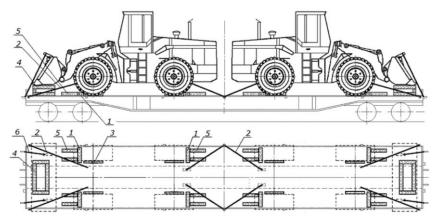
Размещение и крепление на платформе техники с навесным оборудованием:
